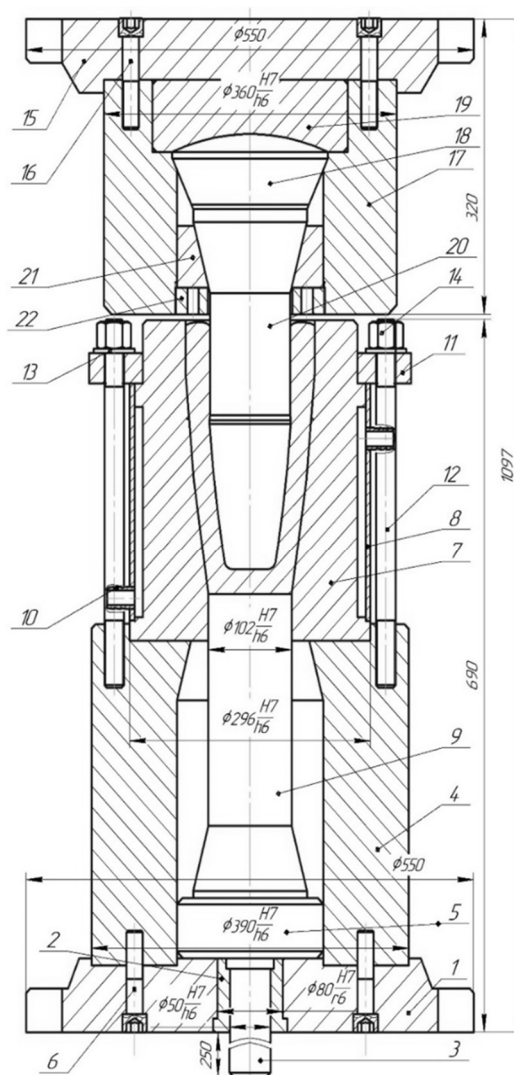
Ескіз загального вигляду штампу для реалізації видавлювання
